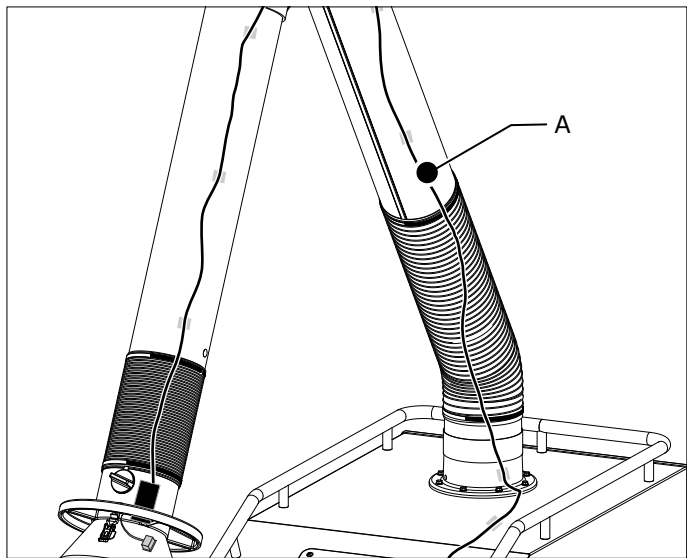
Befestigen des Kabels der Arbeitslampe
